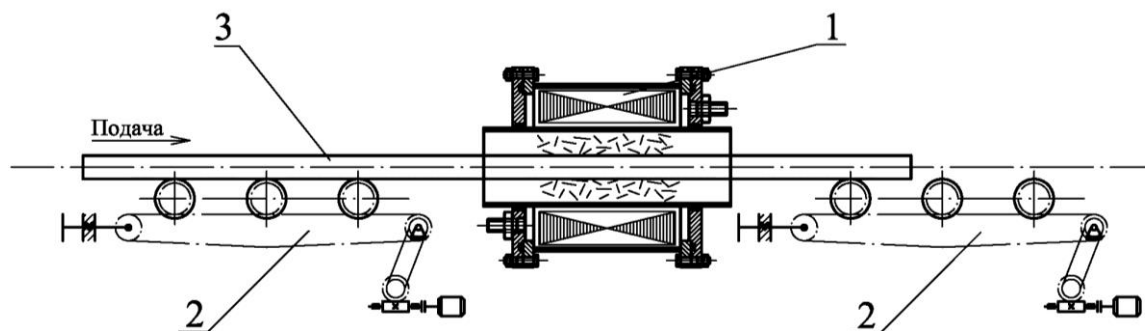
Схема обработки длинномерных деталей: 1 – рабочий блок устройства с ВЭМП; 2 – приводной роликовый рольганг; 3 – деталь
